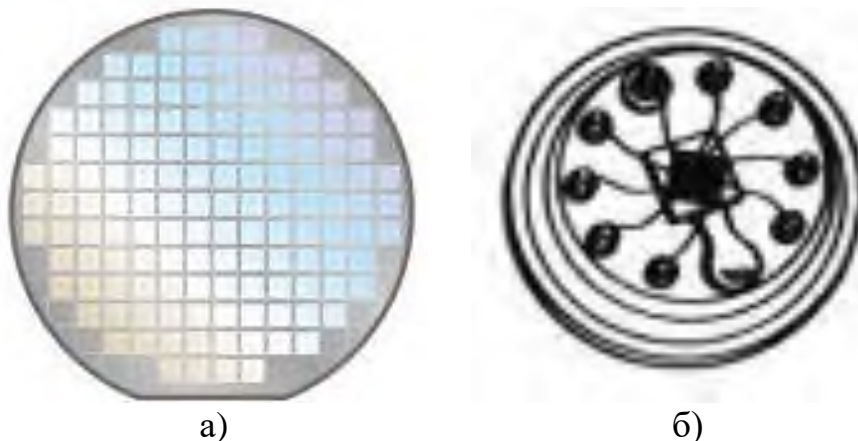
НІМС: а - підкладка; б - з'єднання із зовнішніми виводами корпусу
